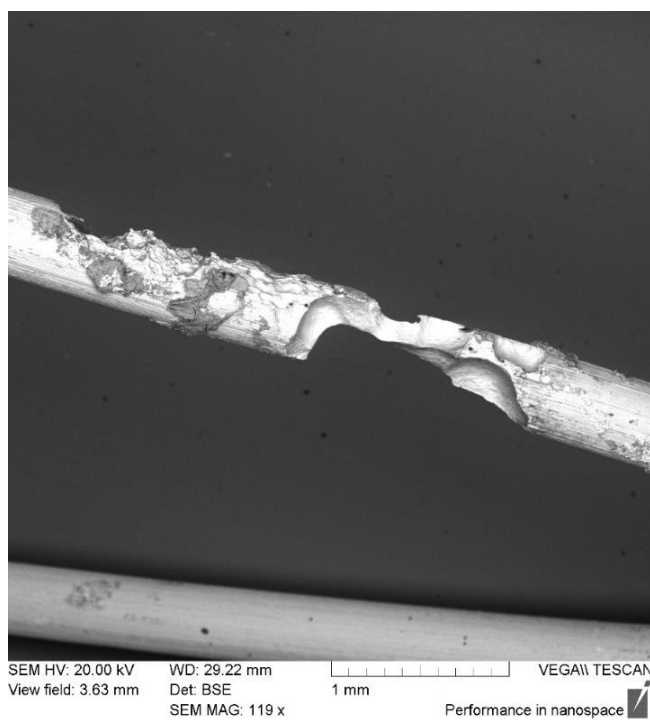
Крупный план повреждений нагревательной спирали тепловентилятора, СЭМ
